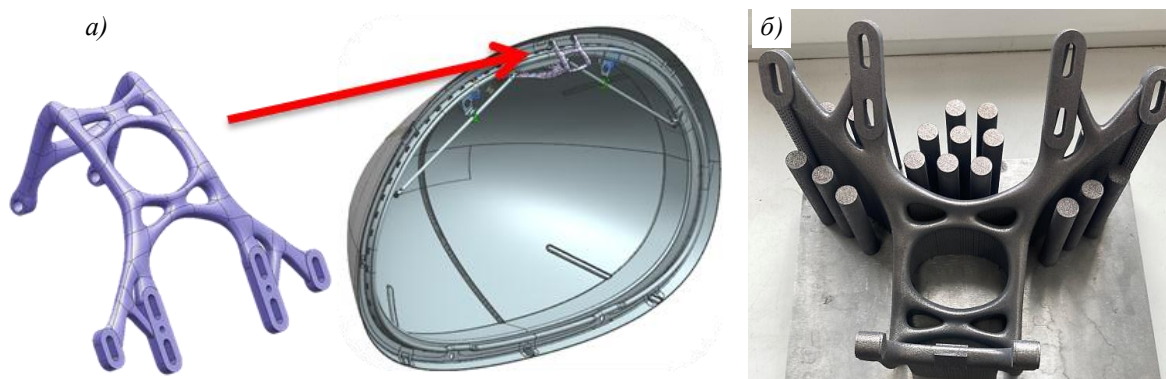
CAD-модель детали для носового обтекателя вертолета (а) и внешний вид заготовки детали с образцами-свидетелями на платформе построения после термообработки (б)
